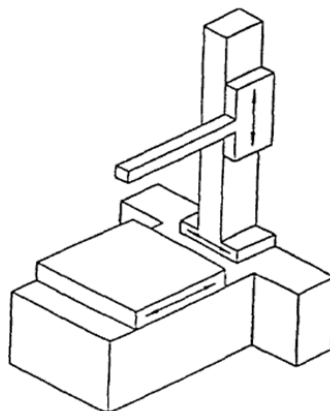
CMM s pevným stolem a vodorovným ramenem [32]
